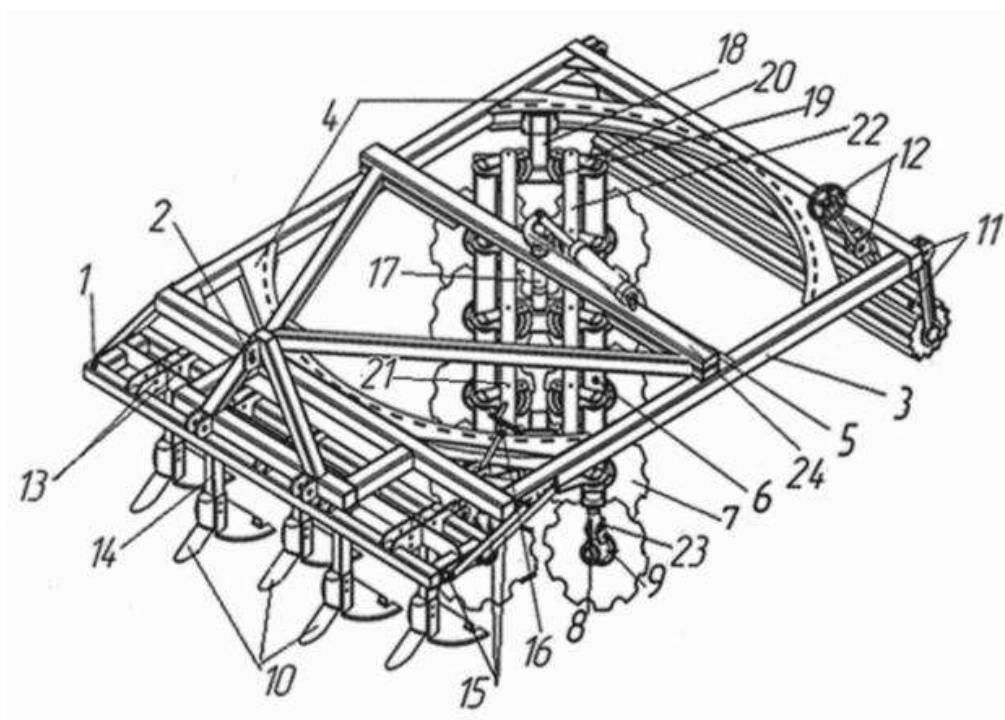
Универсальный плуг с поворотной балкой (вид сверху)
